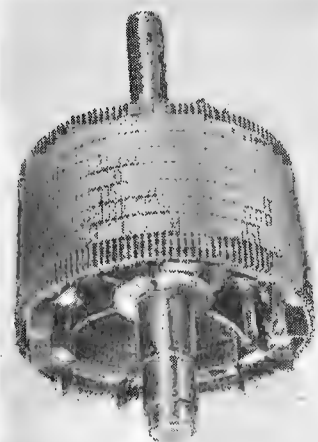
Готовый ротор с беличьей клеткой для большого двигателя.
